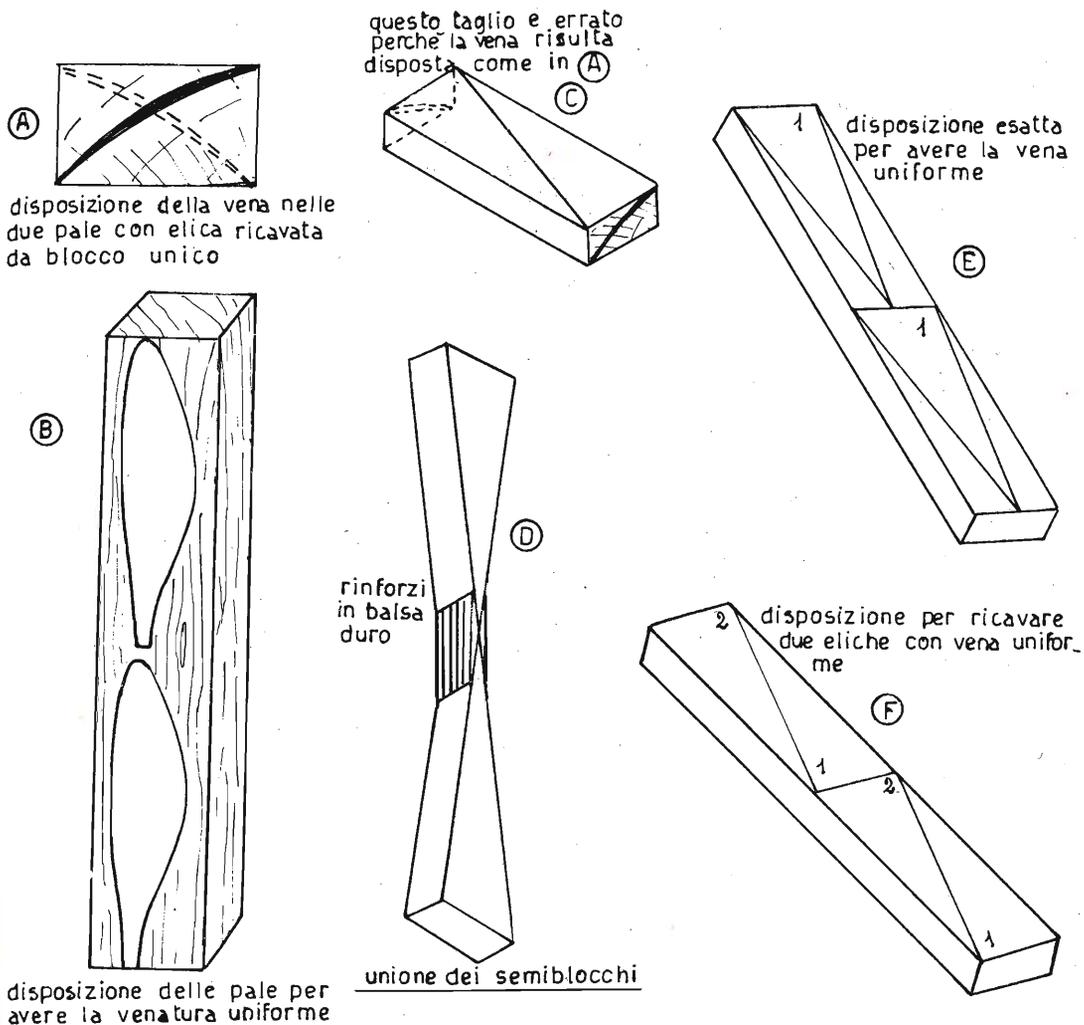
DISPOSIZIONE PALE RICAVATE DAL BLOCCO
